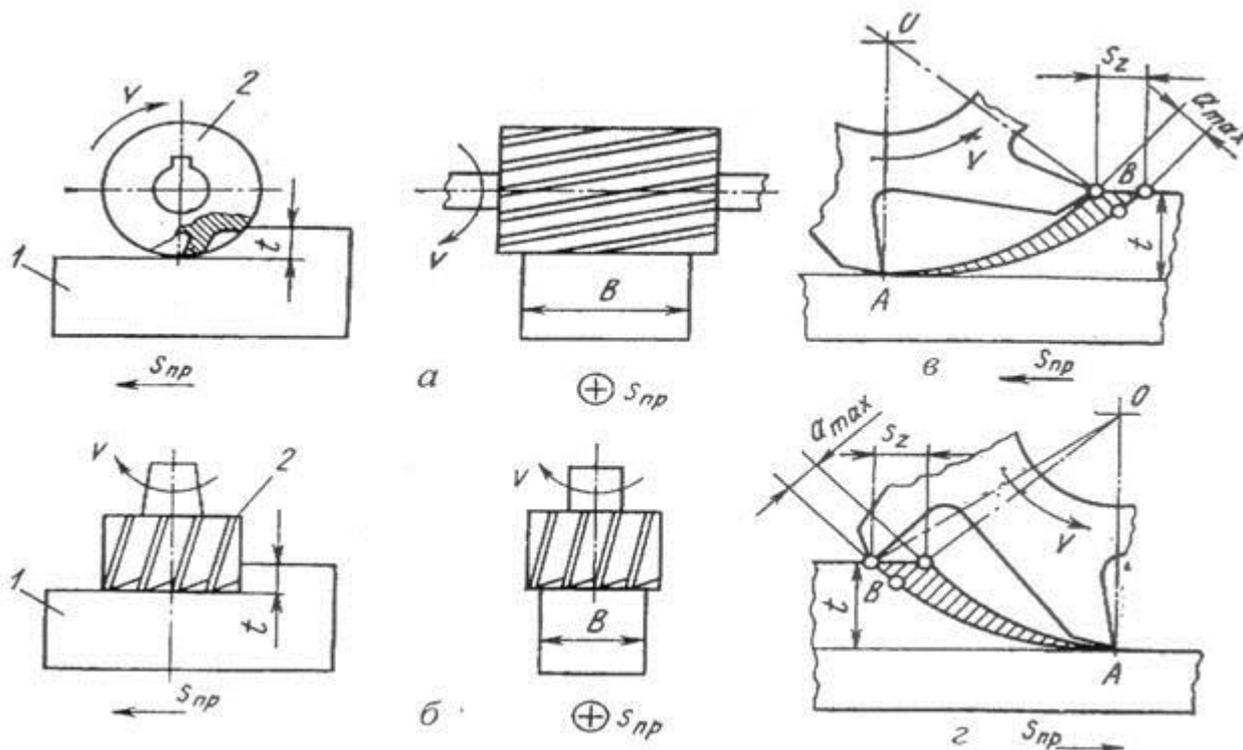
Схемы фрезерования цилиндрической (а) и торцовой (б) фрезами, встречного (в) и попутного (г) фрезерования: 1 – заготовка; 2 – фреза
